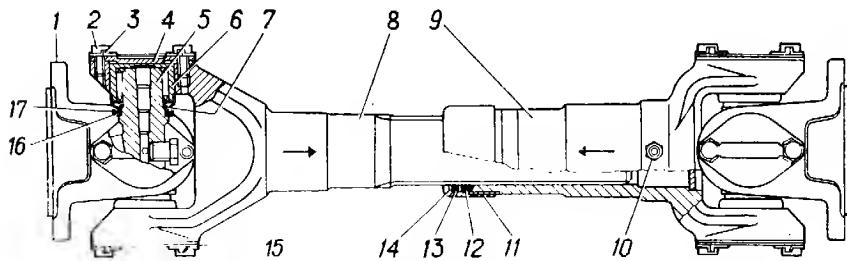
Передний карданный вал привода водометного движителя (вал второго типа):
